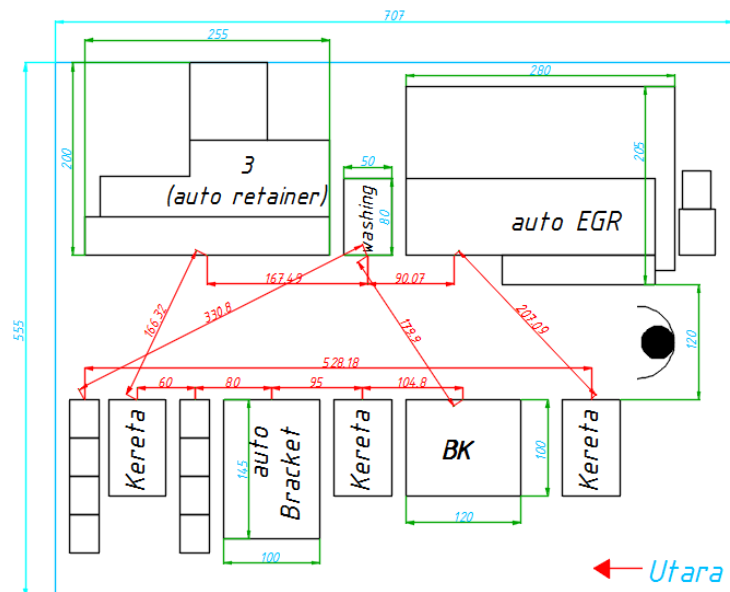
Layout Produksi 1 Gravity Dies Casting
